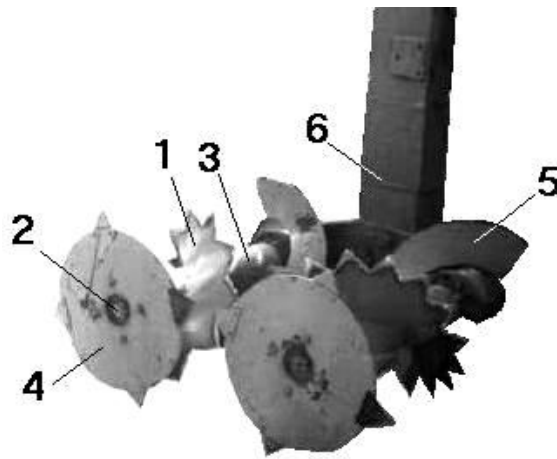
Пило-винтовой рабочий орган с развитыми швыряющими свойствами:
